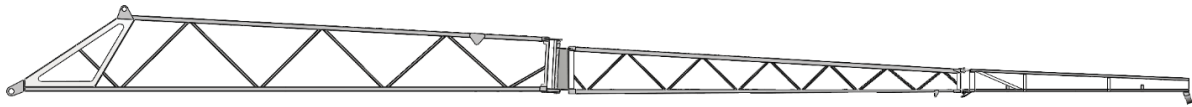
Загальний вигляд штанги широкозахватного польового обприскувача
